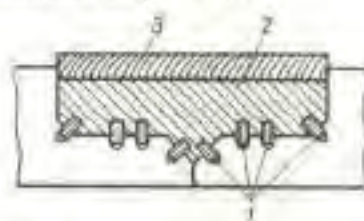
Підготовка чавунного виробу до холодного зварювання з сталевими шпильками: 1 – сталеві шпильки; 2 – сталевий за'їдок; 3 – наплавлення електродом
